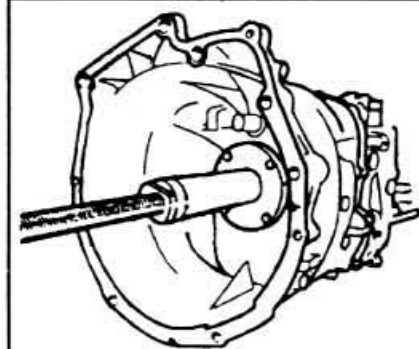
Спрессовка картера сцепления с помощью приспособлений BMW 33 1301 и 23 2280
